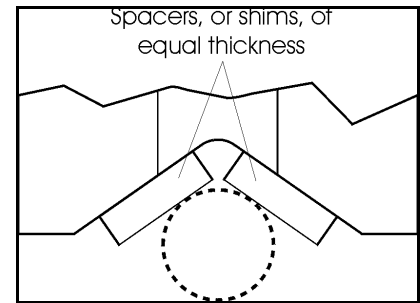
MONTAJE DEL EJE PEQUEÑO
